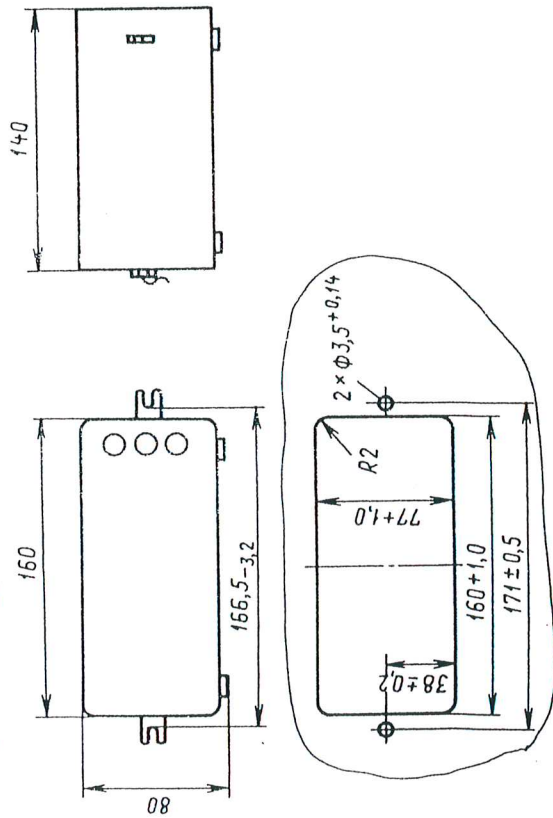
Габаритный чертеж секундомера и разметка шита под установку секундомера СЭЦ-10000Щ
